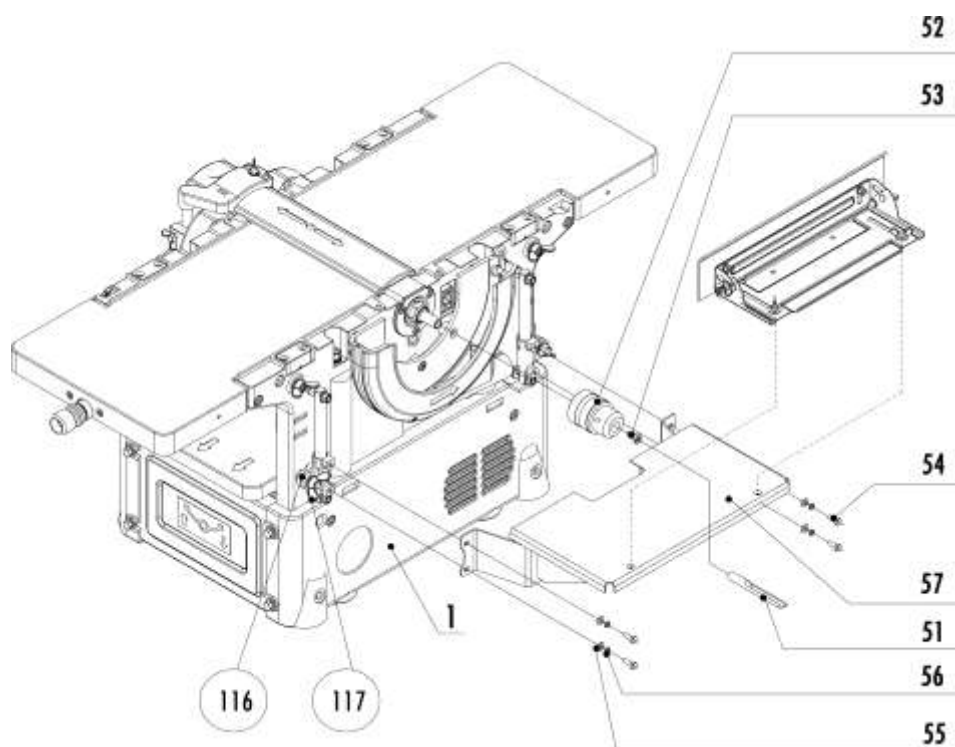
Машина деревообрабатывающая фрезерно-сверлильная.
